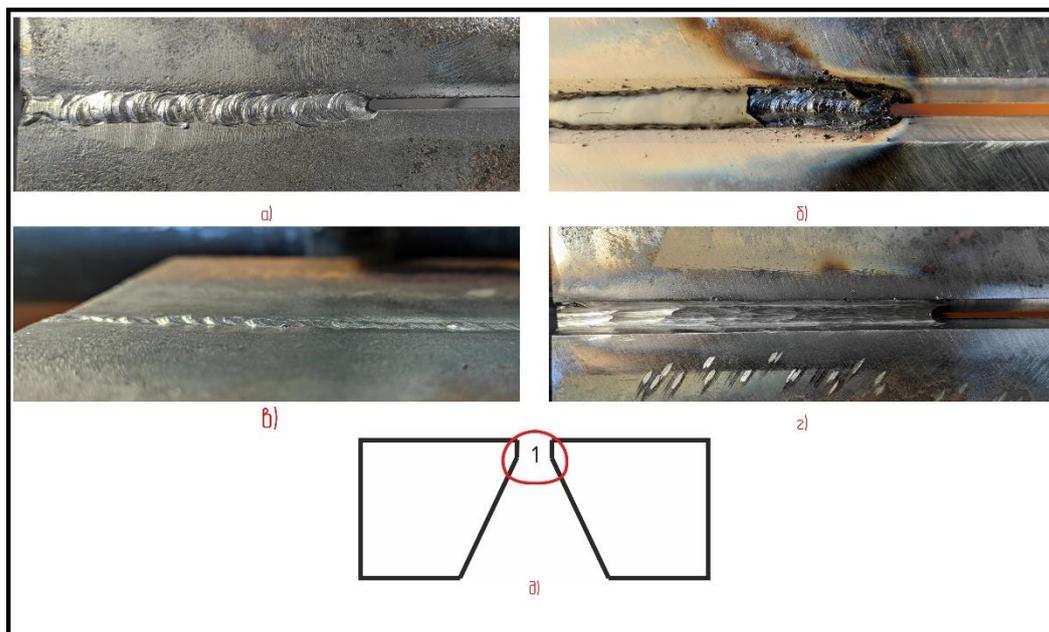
Фотографии корня стыкового шва в положении РЕ: а) Обратная сторона; б) Лицевая сторона; в) Обратная сторона, вид сбоку; г) Лицевая сторона, подготовка поверхности под за-
